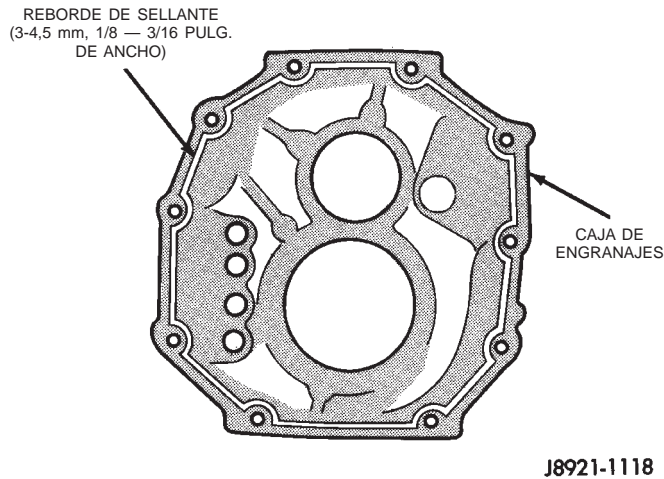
Aplicación de sellante a la caja de engranajes de la transmisión
